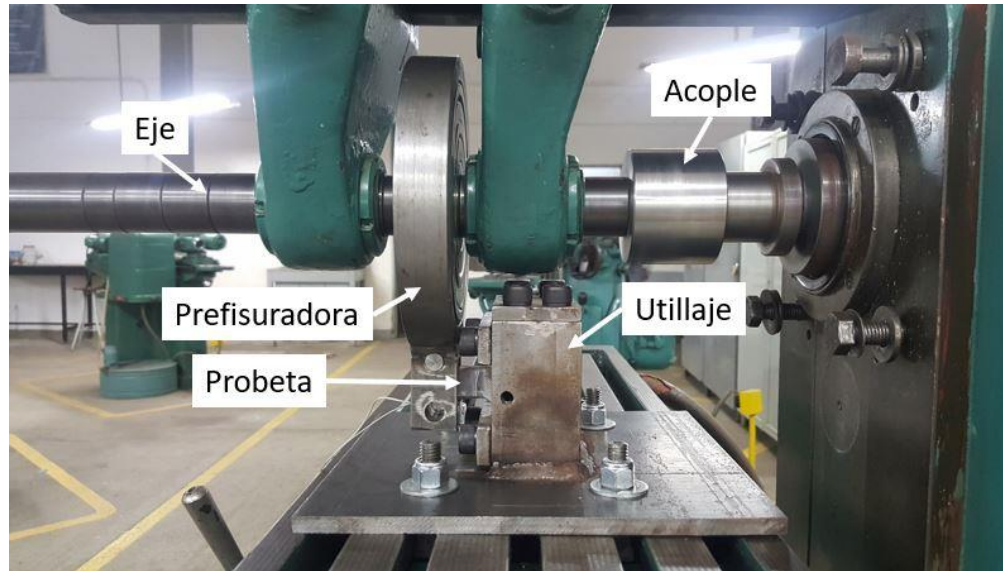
Utillaje montado sobre la fresadora con la probeta de prueba
